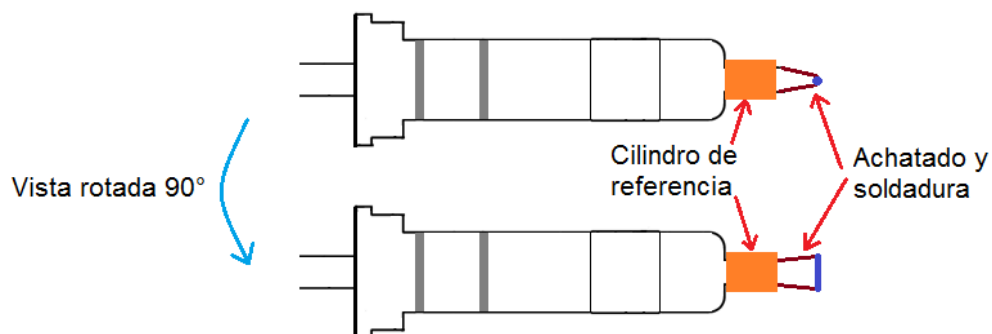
Uso del cilindro de referencia y el achatado de la punta para realizar la soldadura
